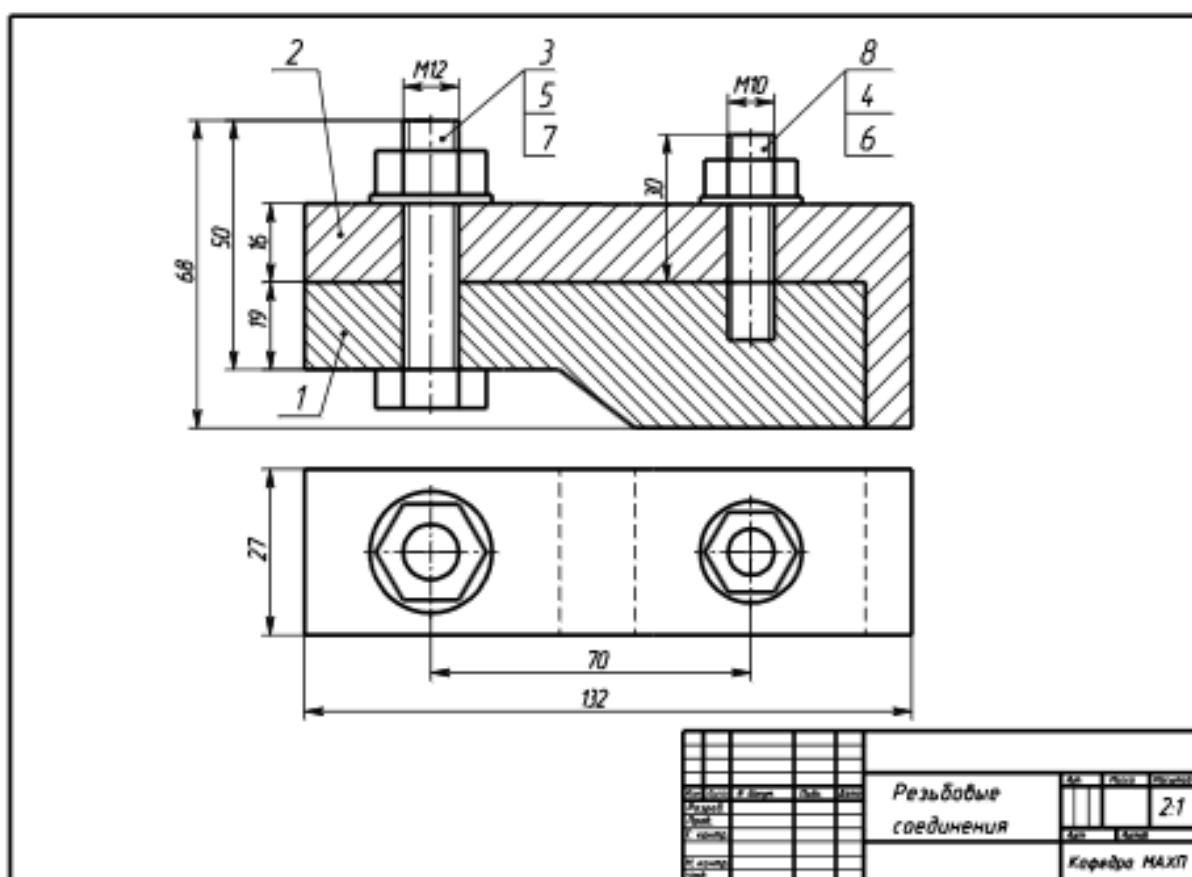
Образец оформления сборочного чертежа по резьбовым соединениям.
